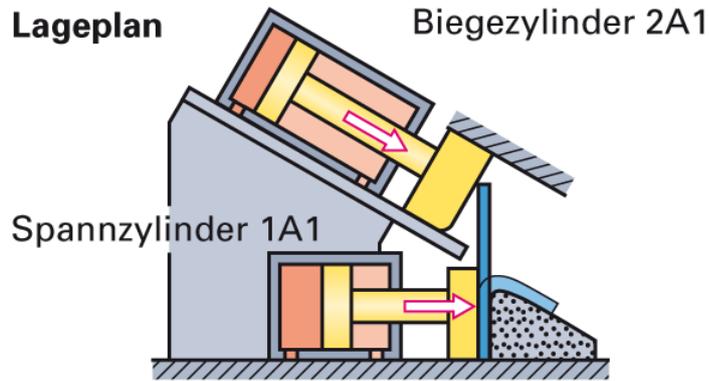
Druckventile in der Steuerung einer hydraulischen Biegevorrichtung
